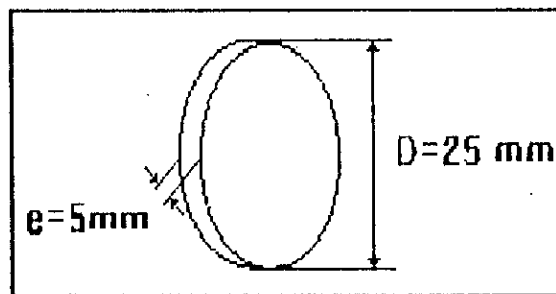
Dimensions de l'éprouvette étudiée.
